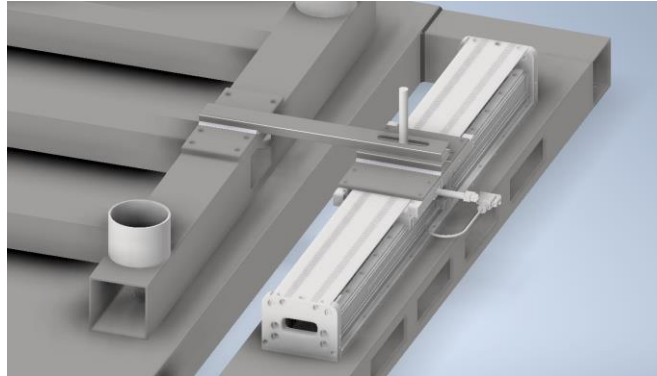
Versió actual per la transmissió de moviment del motor lineal
